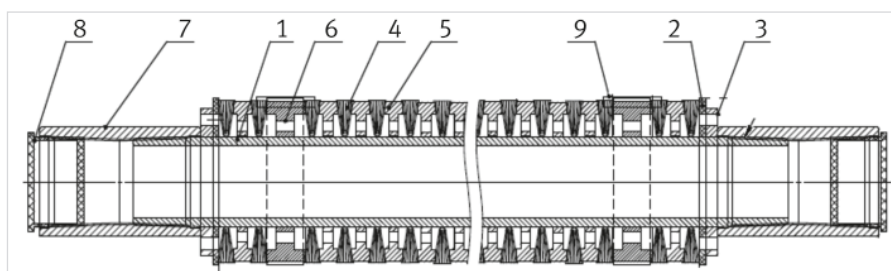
Щеточный фильтр: 1 — патрубок; 2 — прокладка уплотнительная; 3 — кольцо упорное; 4 — фильтроэлемент; 5 — прокладка стальная; 6 — прокладка под клямсу; 7 — муфта; 8 — заглушка муфты; 9 — клямса ППК
